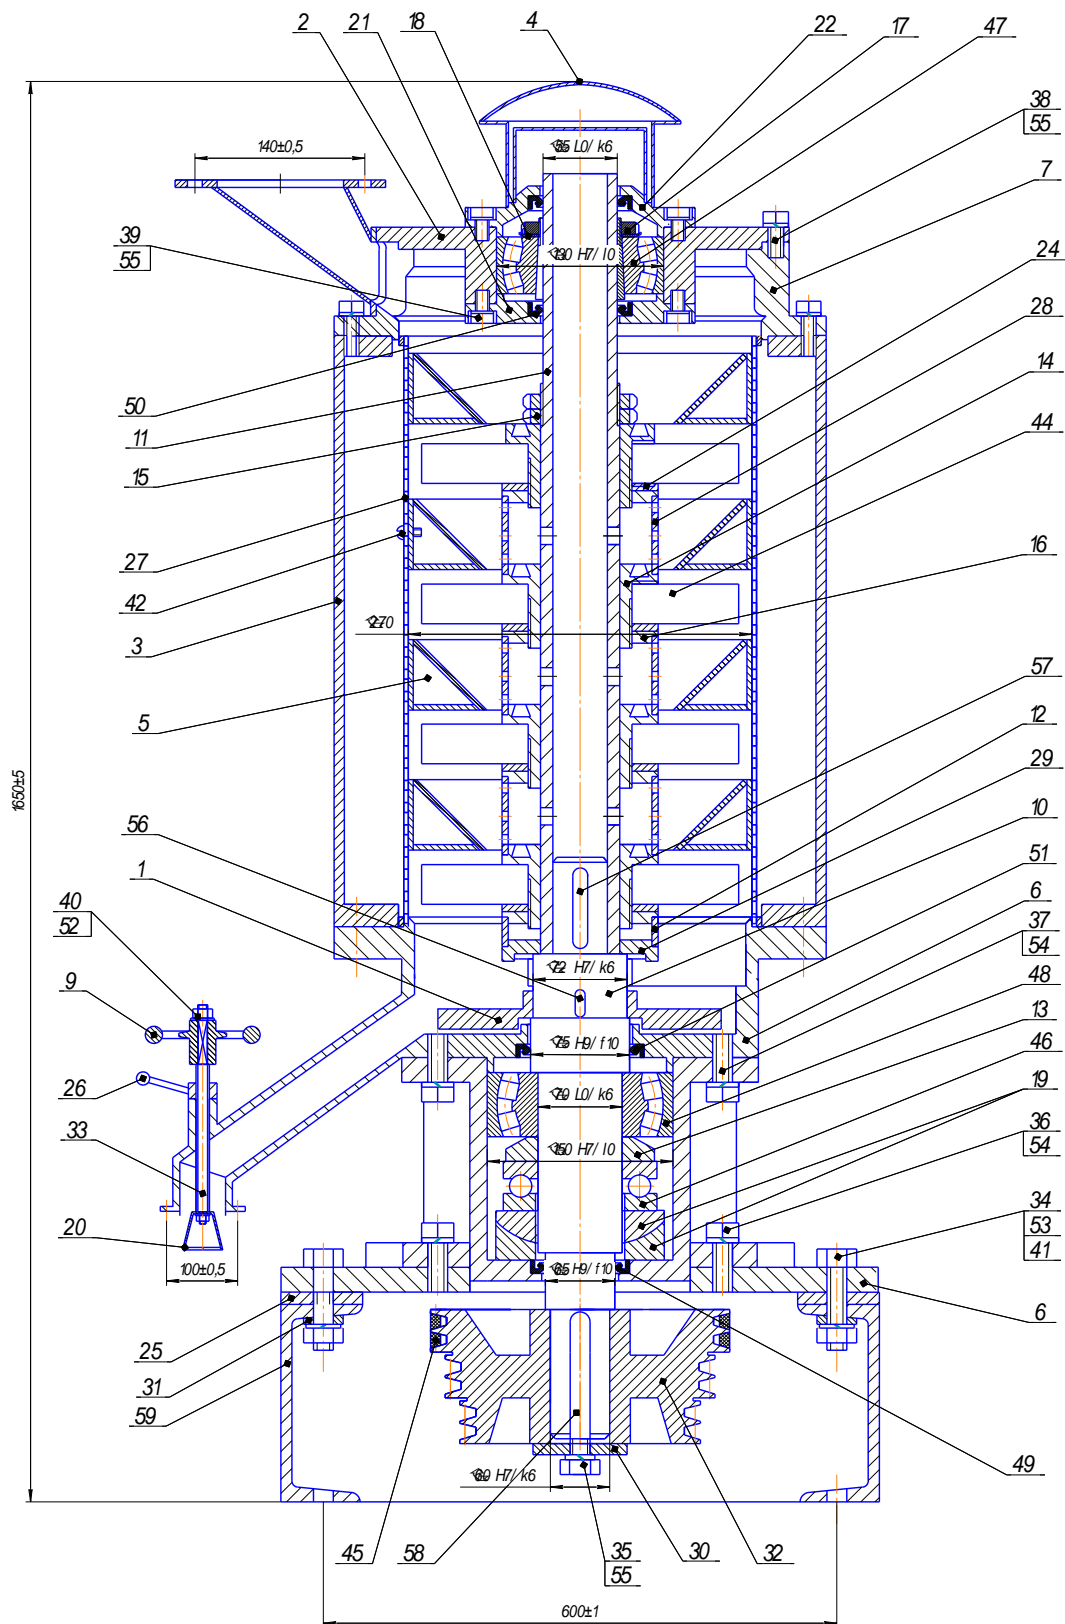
Луцильно-шліфувальна машина: 1 – викидач, 2 – головка; 3 – каркас, 4 – кришка; 5 – конус; 6 – плита; 7 – опора верхня, 8 – опора нижня; 9 – штурвал; 10 – вал, 11 – вал пустотілий; 12,13,14- втулка; 15,16,17-гайка; 18 – кільце стопорне; 19- компенсатор; 20 – конус; 21, 22 – кришка; 23 – патрубок; 24 – прокладка; 25 – плат; 26 – ричав; 27, 28 – сітка; 29, 30, 31 – шайба; 32 – шків; 33 – штанга; 34-39 – болт; 40,41 – гайки; 42, 43 – гвинт;44-48 – підшипник; 49-51 – манжети; 52-55 – шайби; 56-58 –шпонки; 59-швейлер
